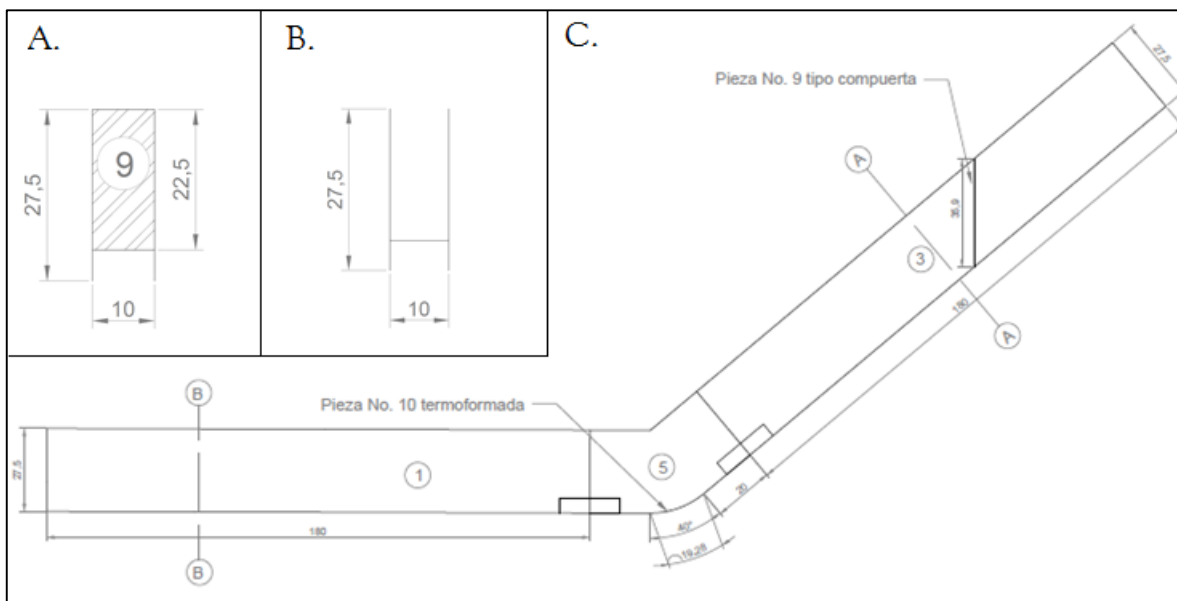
Montaje general del canal Collapses V1.0 mediante la unión de las piezas de la Figura 46: A. Corte A – A de la parte C, B. Corte B – B de la parte C, C. Vista lateral del canal Collapses V1.0
